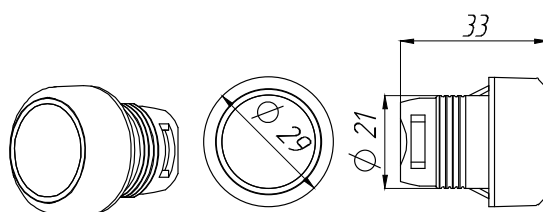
Общий вид и габаритные размеры корпуса кнопки пуск SB1 MP1-10G
